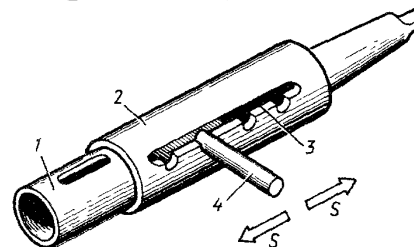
Байонетна оправка для глибокого свердління:
